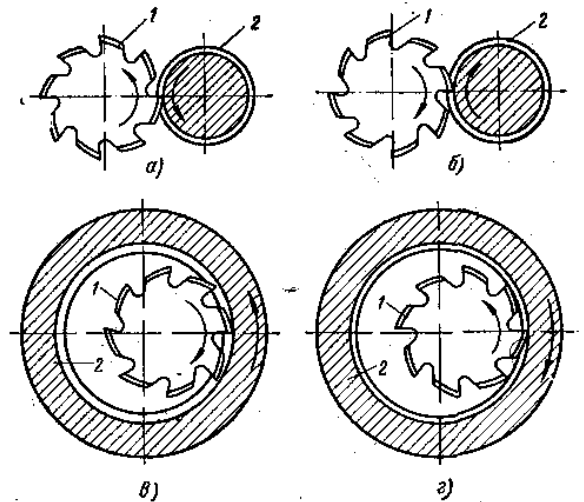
Направление вращения фрезы и заготовки при фрезеровании резьбы: а — правая наружная, б — левая наружная, в — правая внутренняя; 2 — левая внутренняя; 1 — фреза, 2 — заготовка
